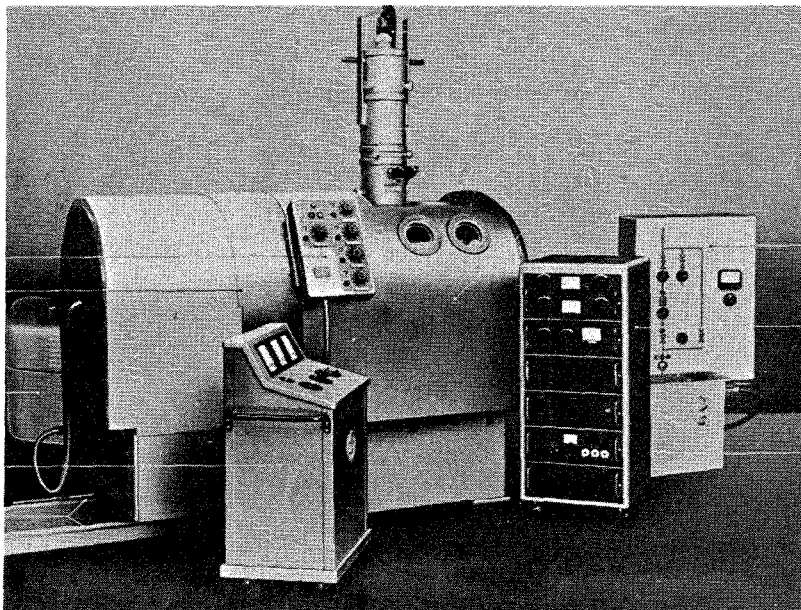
Elektronenstrahl-Schweißanlage ES1013
